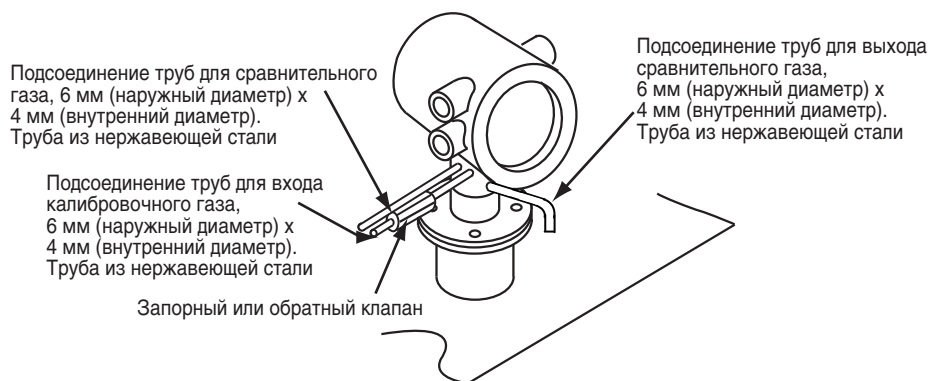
Подсоединение труб к входу калибровочного газа
